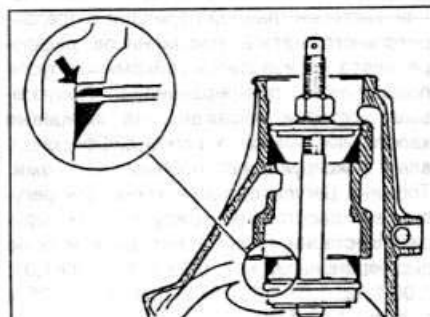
Установка наружного кольца внутреннего подшипника ведущей шестерни с дистанционным кольцом (показано стрелкой) при помощи приспособления 15.083
